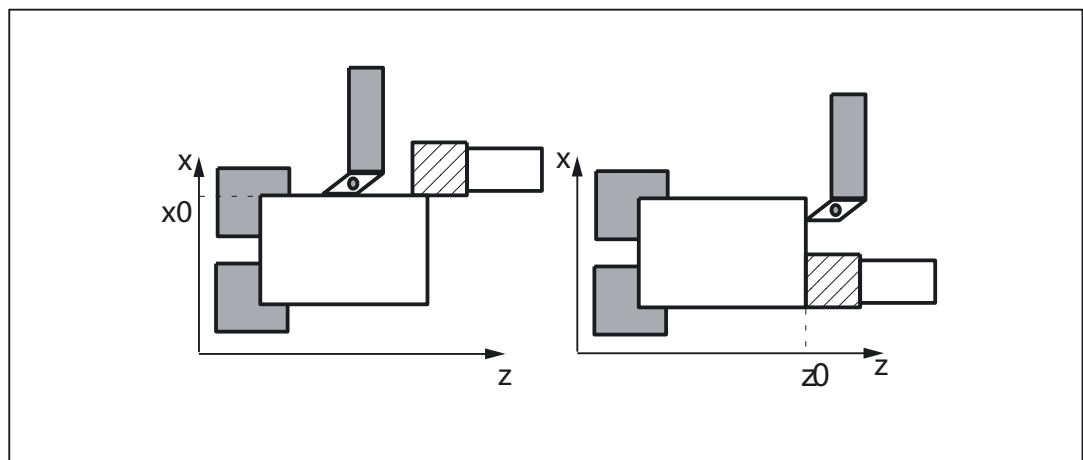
Messen einer Werkzeuglänge mit gemerkter oder aktueller Position
